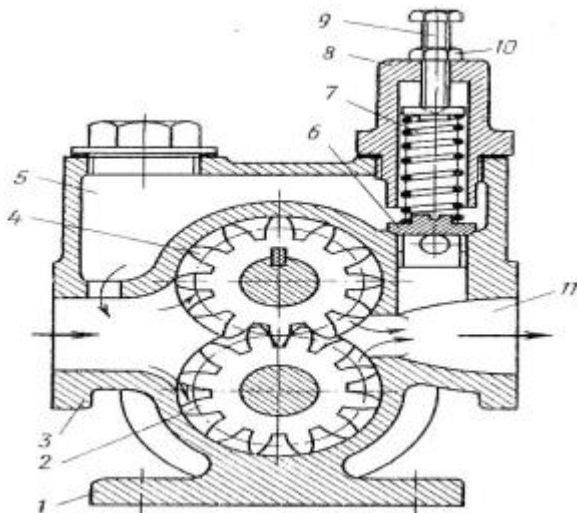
Устройство и схема работы шестеренного насоса с редукционным клапаном: 1 - корпус; 2,4 - зубчатые колеса (шестерни), 3 - приемный патрубок; 5 - перепускная полость; 6 - клапан; 7 - пружина; 8 - корпус клапана; 9 - регулировочный болт; 10 - контргайка; 11 - нагнетательный патрубок.
